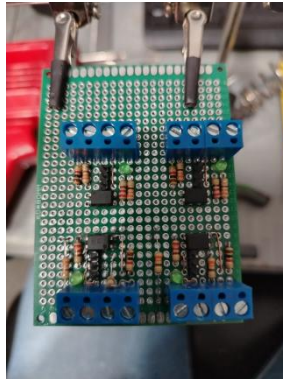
Tarjeta opto-acoplador, imagen del autor
